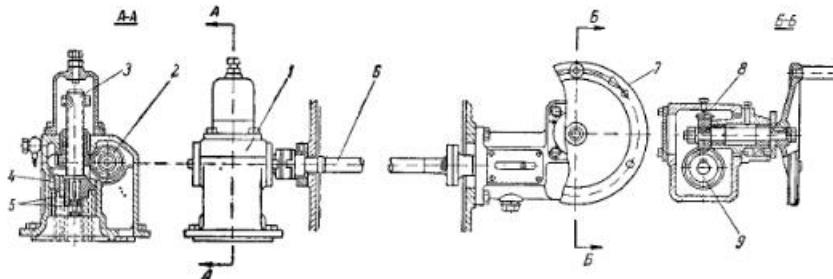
Привод для изменения числа оборотов двигателей типа NVD-48:
